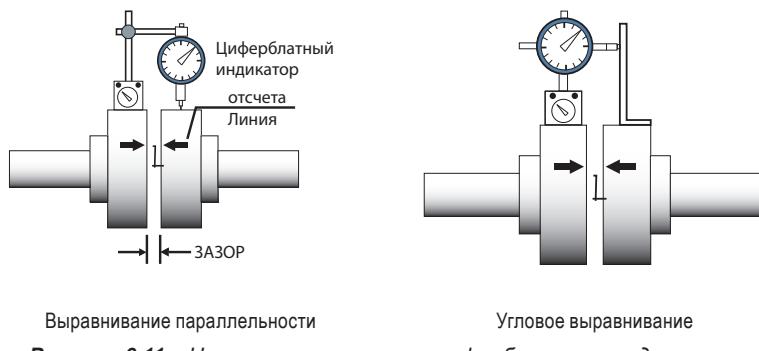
Центровка с помощью циферблатного индикатора.
